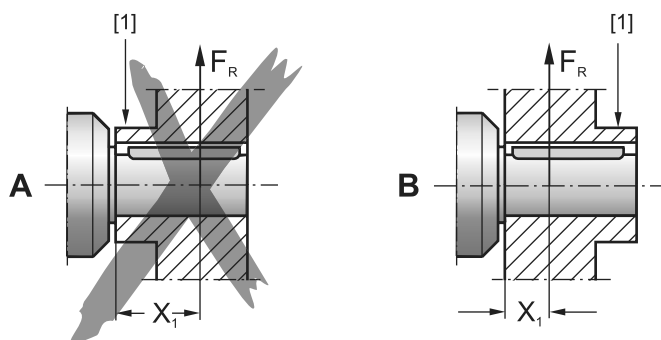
Disposição de montagem correcta de uma polia ou roda dentada
